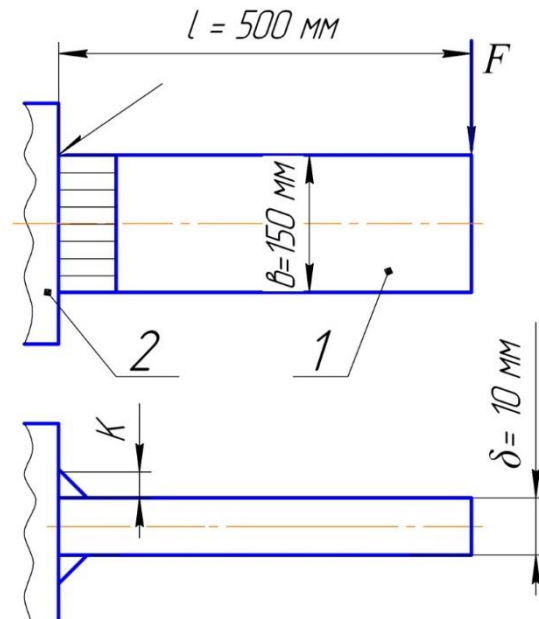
Крепление балки к колонне: 1 – балка; 2 – колонна
